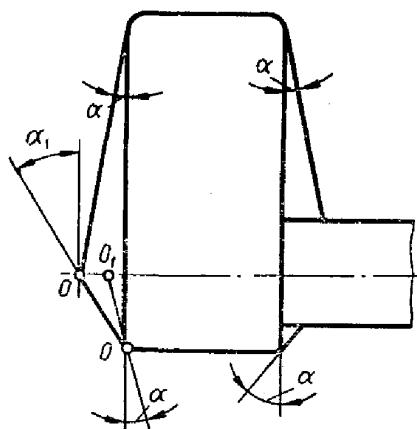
Корегування кута штампувального нахилу при несиметричному (щодо поковки) розташуванні поверхні роз'єднання
